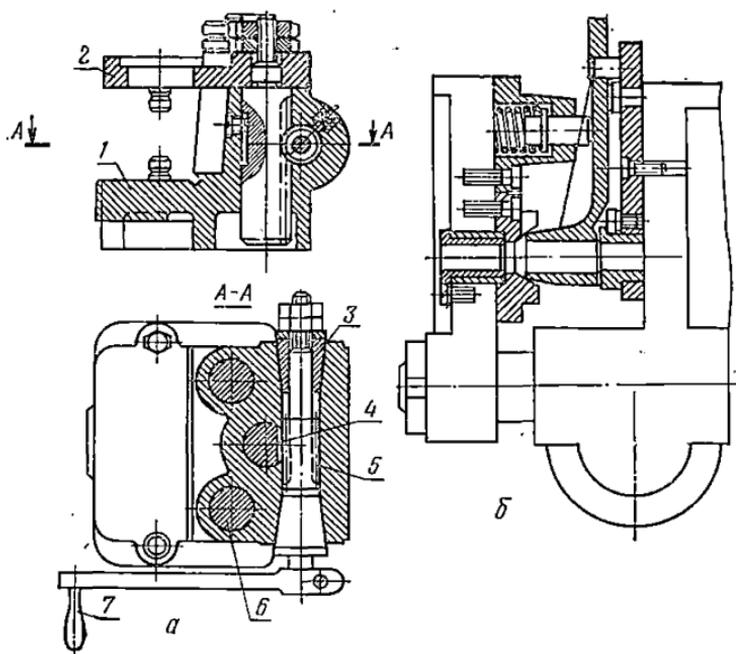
Скальчатый кондуктор (а) и его наладка (б) для сверления отверстия в рычаге (вид б повернут на 90°):
